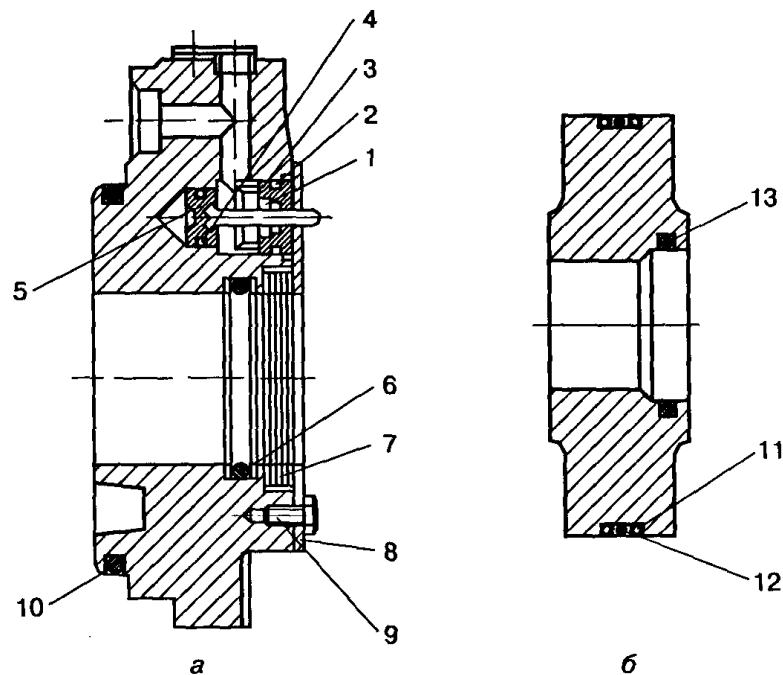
Передняя крышка (а) и поршень (б) гидравлического цилиндра: 1 – втулка; 2,4,6,10,12,13 – кольцо уплотнительное; 3 – корпус клапана; 5 – клапан; 7 – чистики (20 шт); 8 – крышка; 9 – винт (6 шт).
